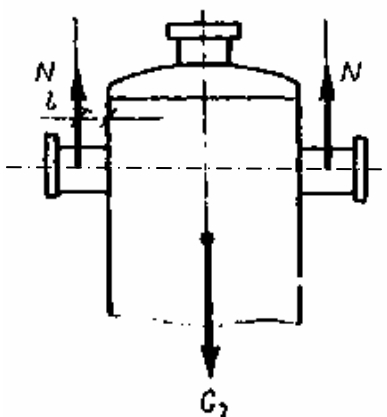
Схема к расчёту монтажных штуцеров
